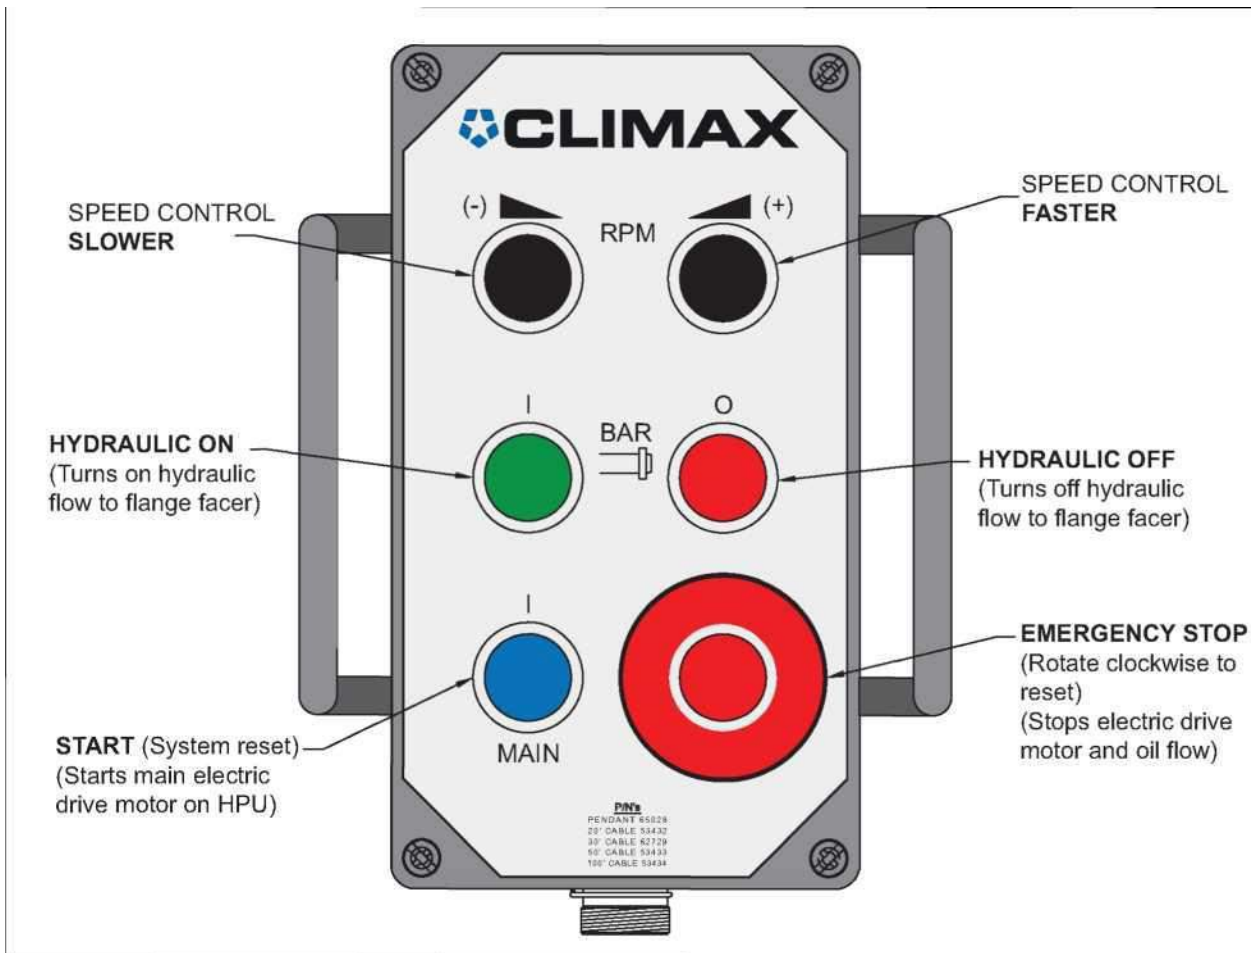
Detail der Steuerung des Hydraulikaggregats
